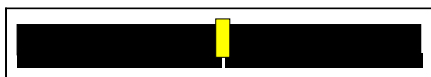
Stumpf mit Heizelement geschweißte Platten.
